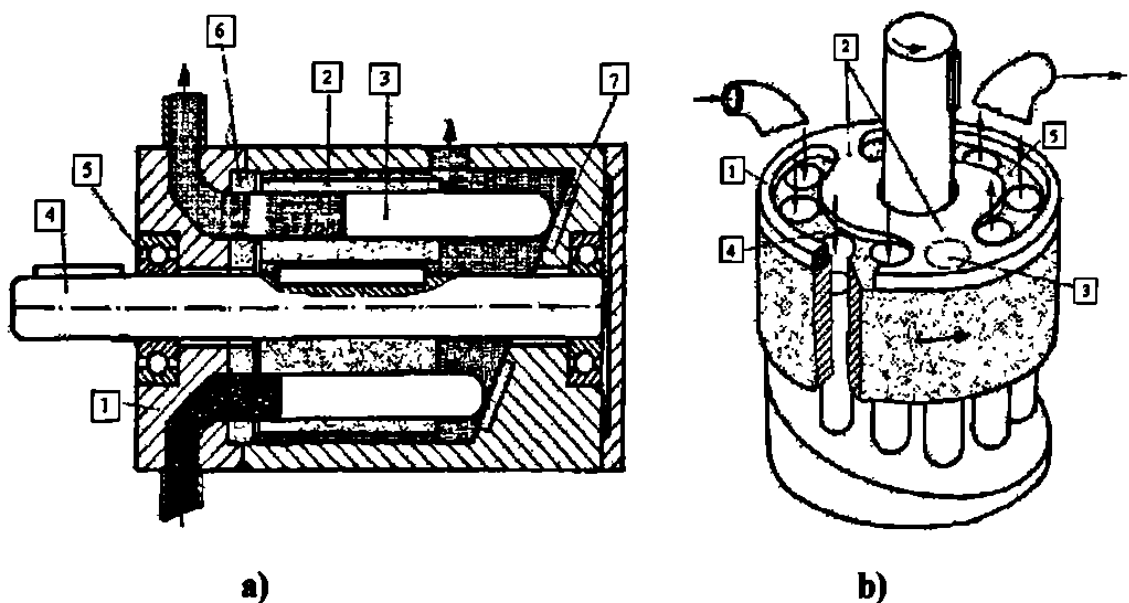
Motor de émbolos axiales con disco inclinado.
